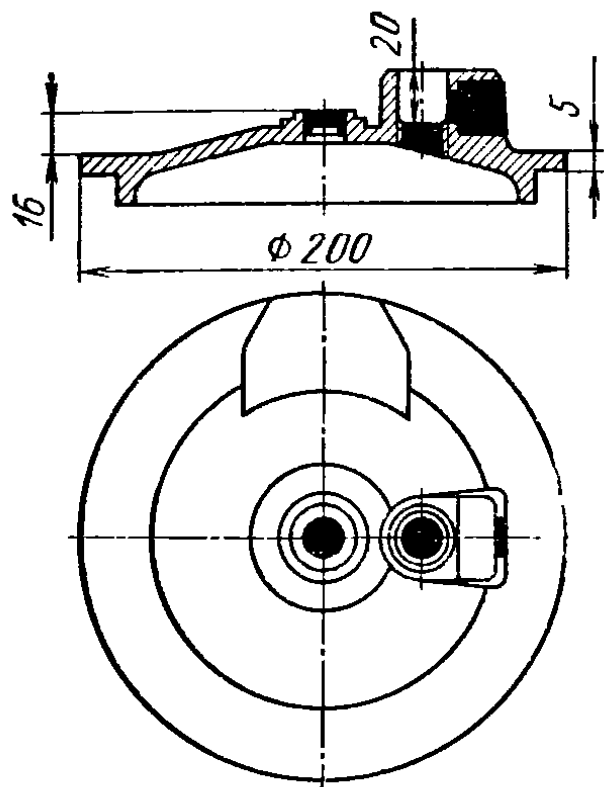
Деталь-крышка, полученная методом полужидкой штамповки
